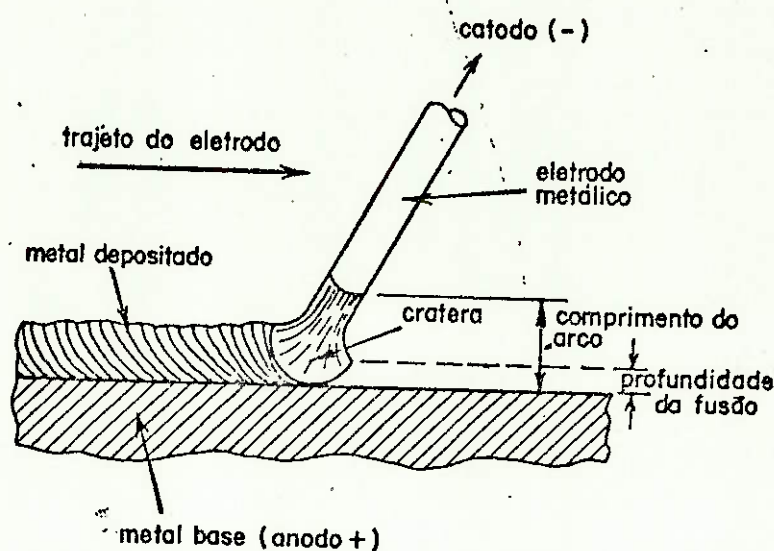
SOLDAGEM A ARCO ELÉTRICO
